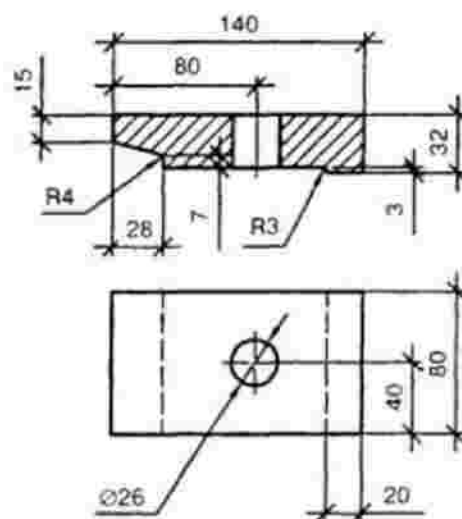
Прижимы для скрепления рельсов с железобетонными балками
